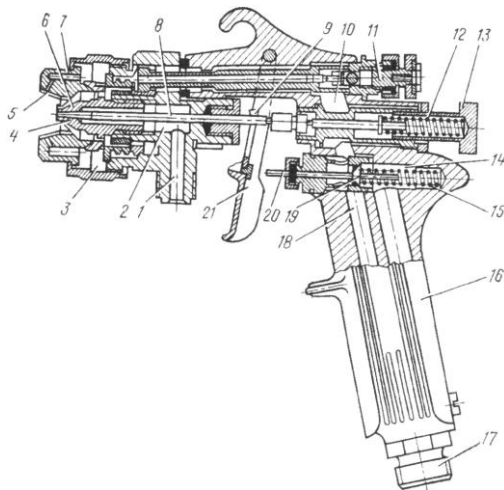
Пневматичний розпилювач ЗИЛ зовнішнього змішування:
